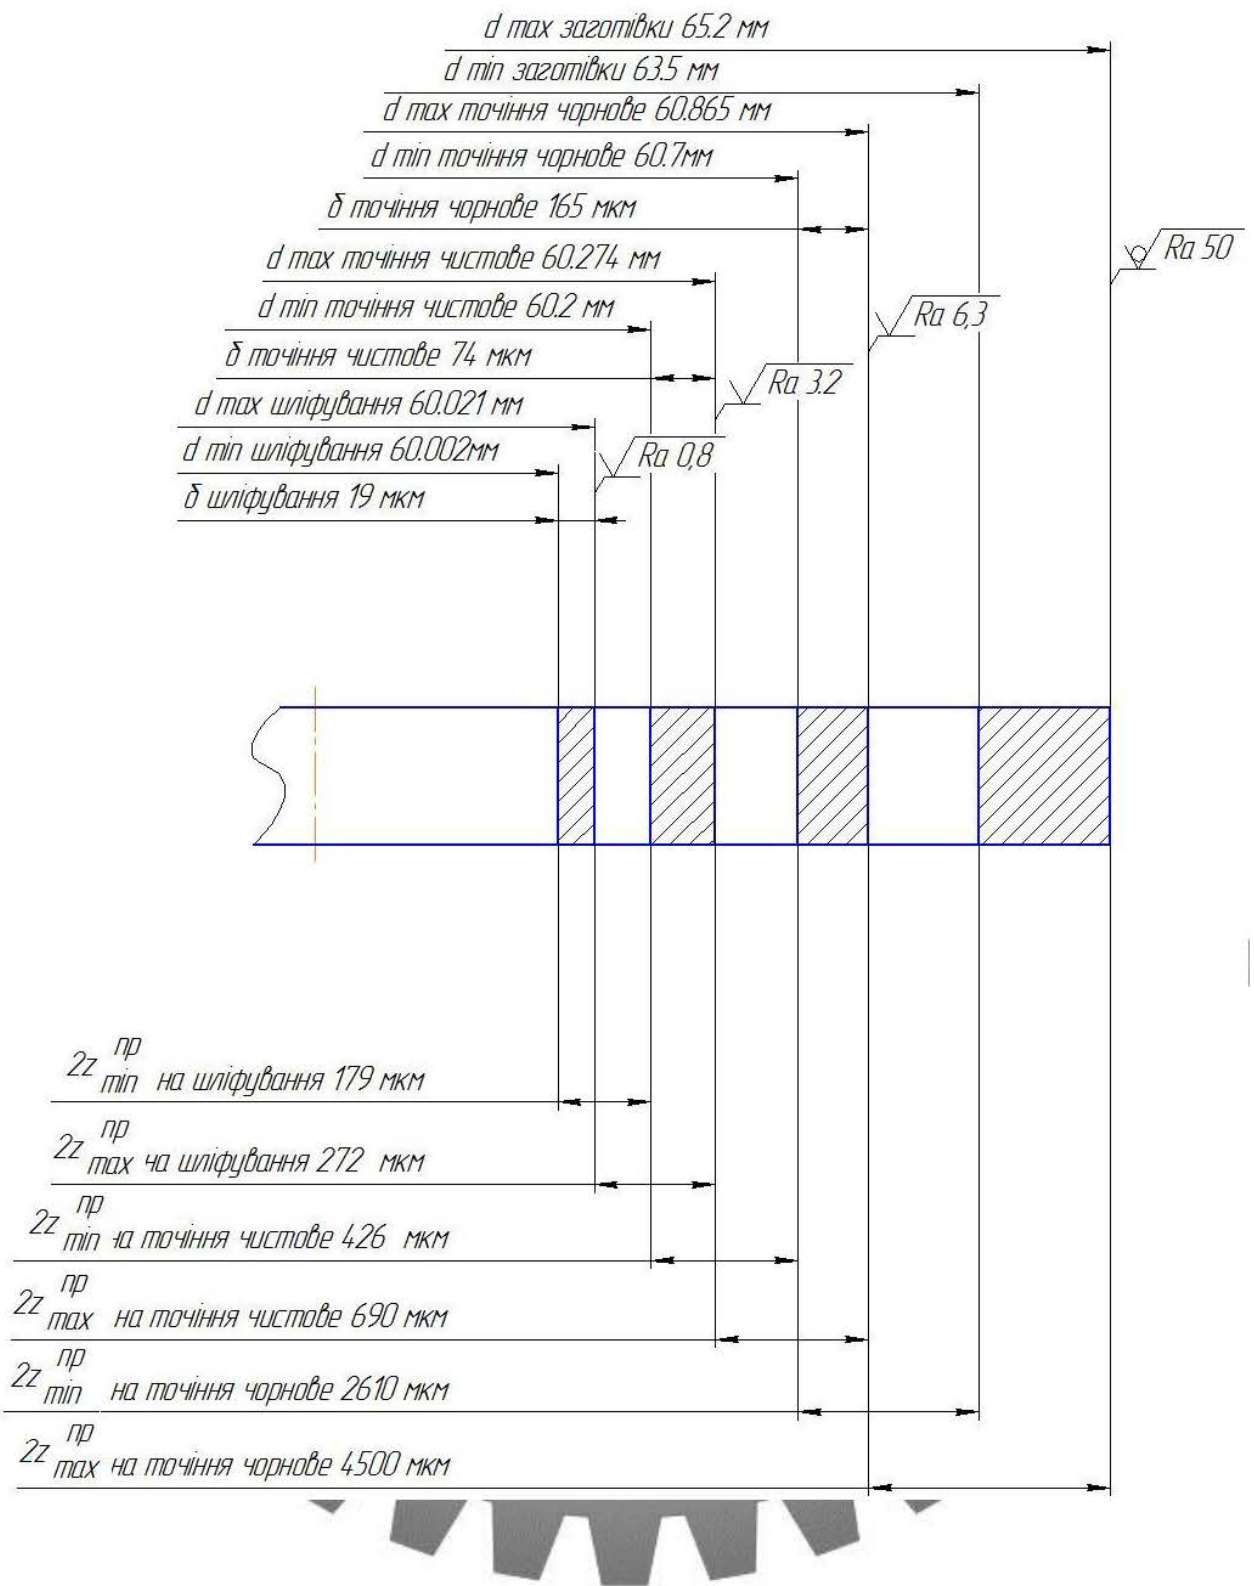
Схема розміщення припусків із допусками при виготовленні діаметрального розміра $\phi 60k6$ вала ведучого
